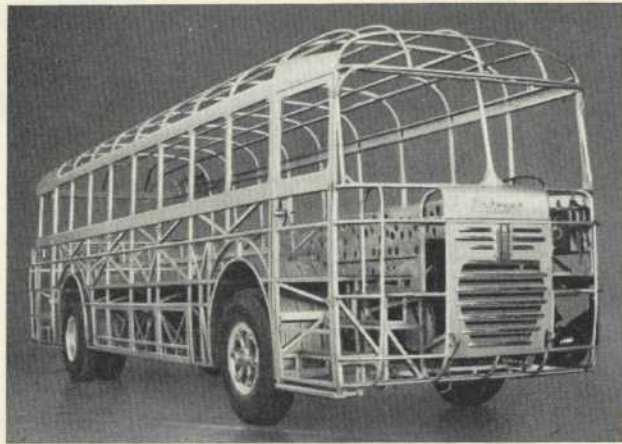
Struttura portante realizzata con saldatura ossi-acetilenica.
